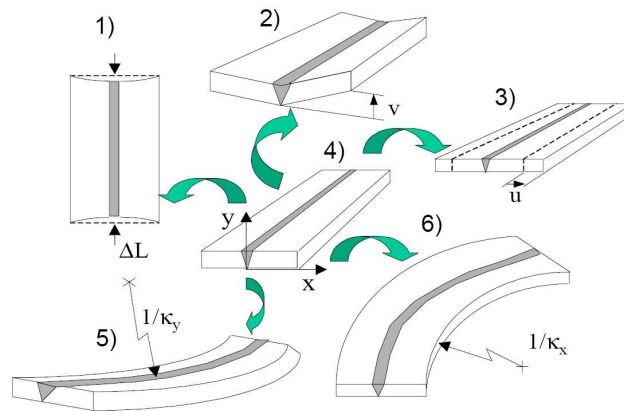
Modos básicos de deformação de placa rectangular com soldadura central
